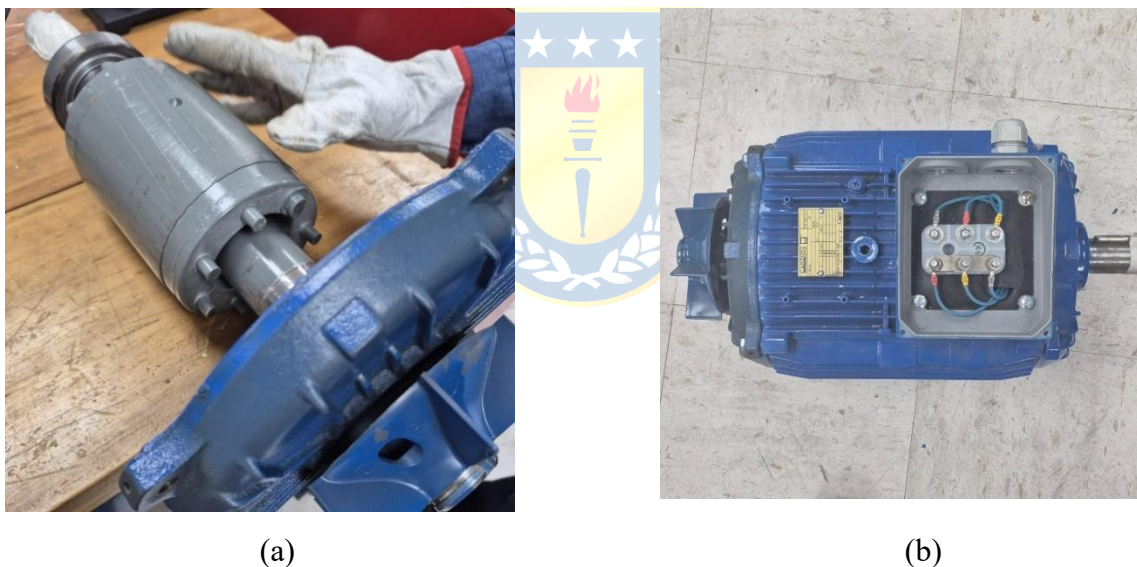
Fotografías Motor 3; (a) Rotor con Barra rota, (b) Motor.
